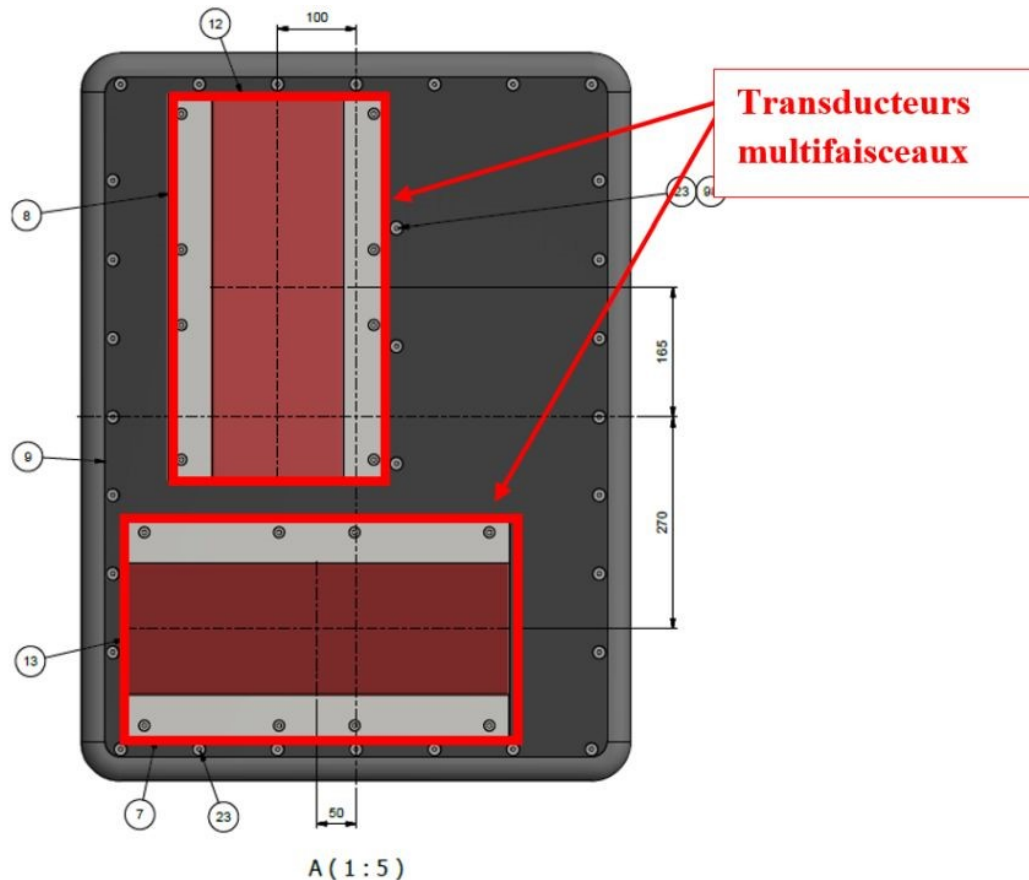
Vue de dessous de l'ensemble du module de transducteur
